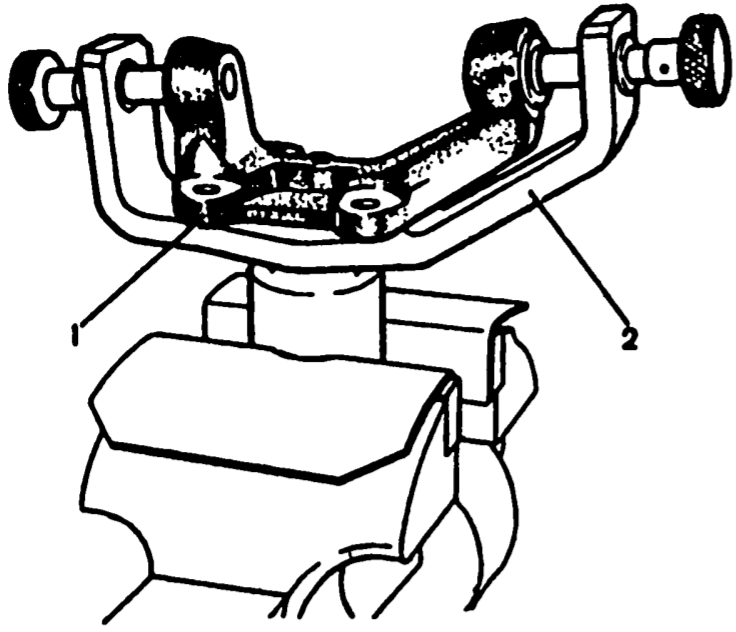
Проверка поворотного кулака: 1 - поворотный кулак; 2 - калибр А.96008
